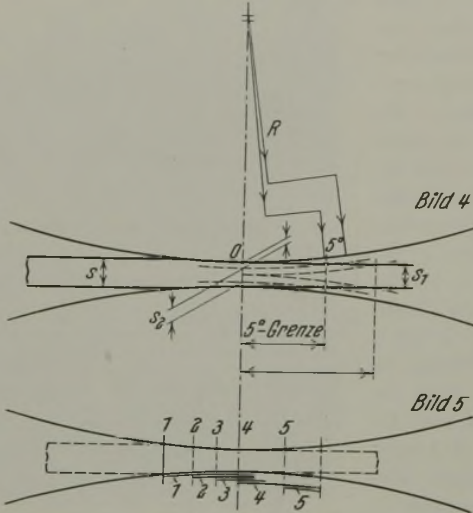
und 5. Vorgang im Walzspalt und Kennzeichnung der mit dem Walzdruck belasteten Flächen.
